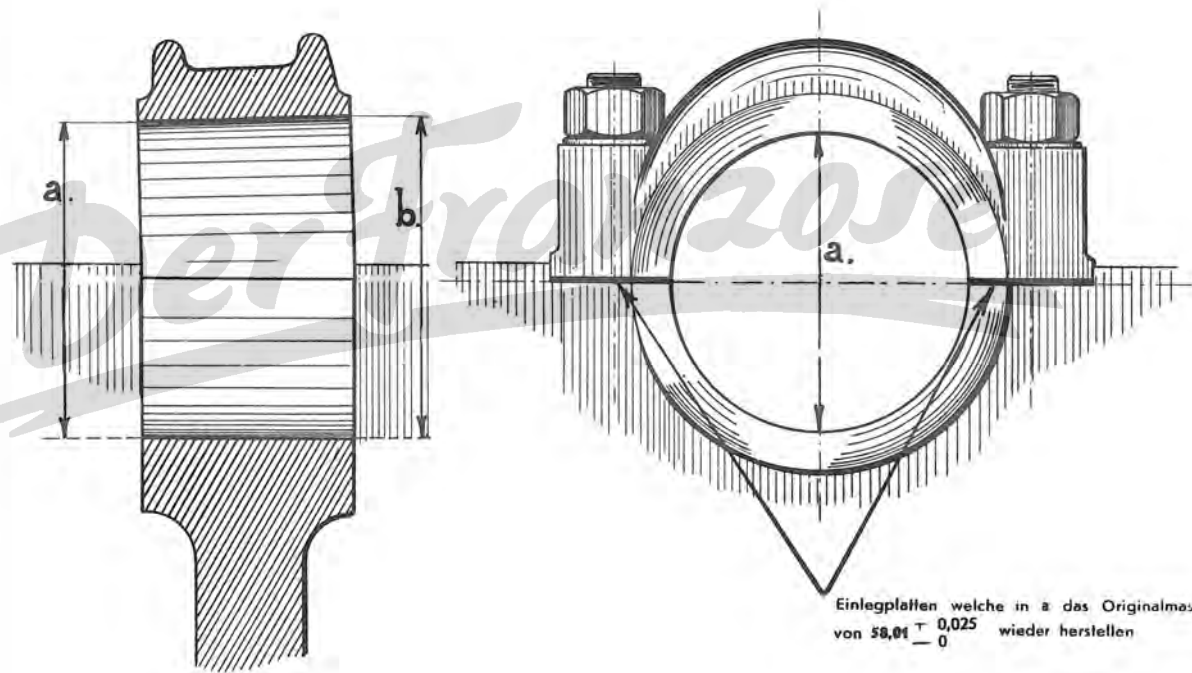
FRÄSEN DER AUFLAGEFLÄCHE
